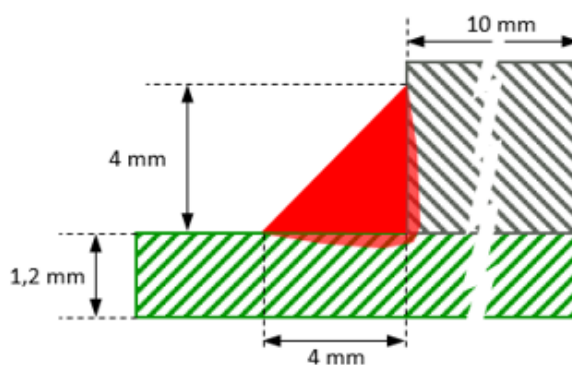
Detalhe da junta soldada com as dimensões mínimas do depósito de solda. A área verde representa o tubo e área cinza a flange.
